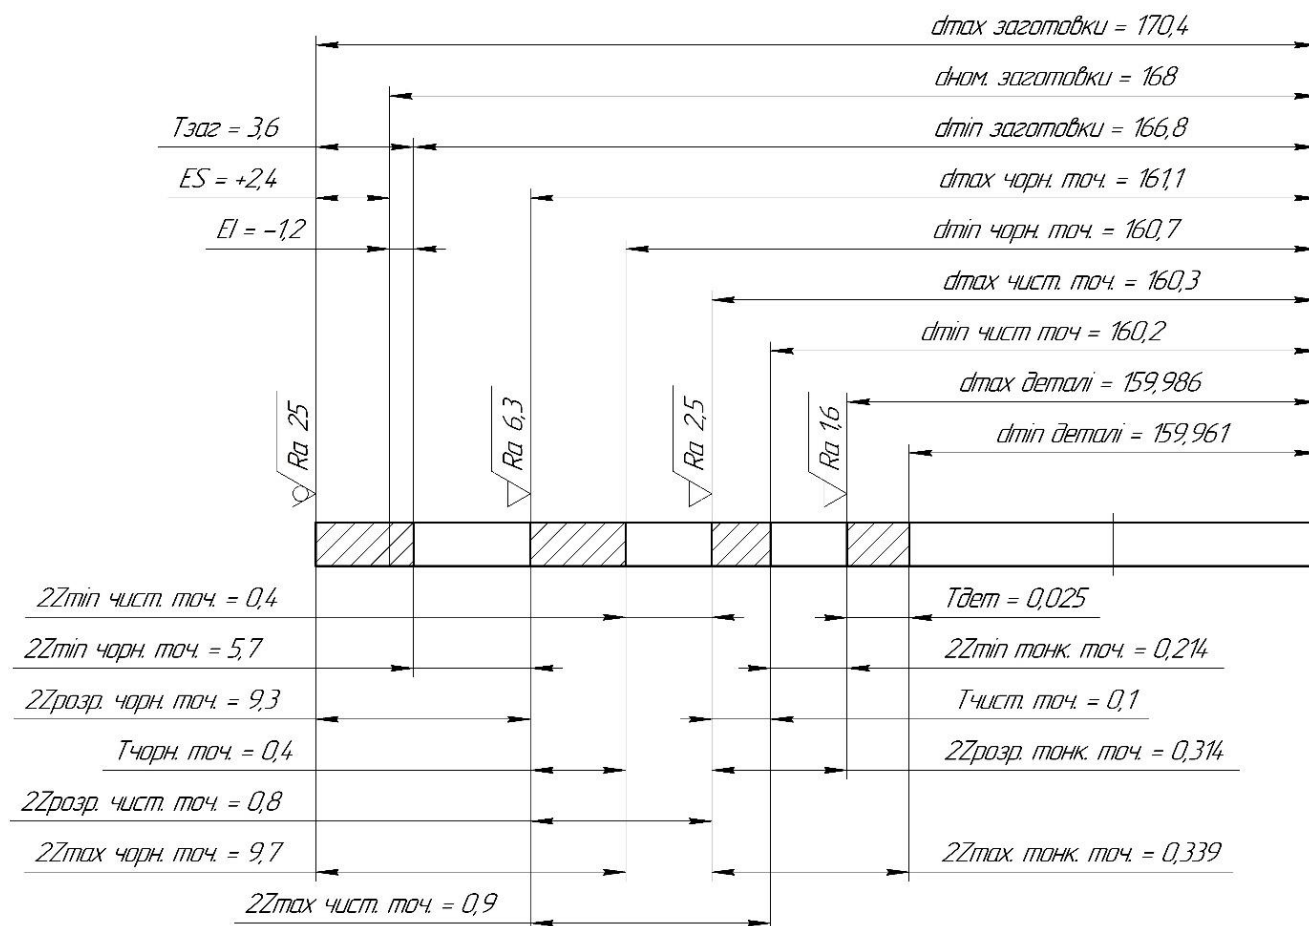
Схема розташування припусків і допусків на обробку поверхні $\varnothing 160g6(-0,014; -0,039)$ мм
